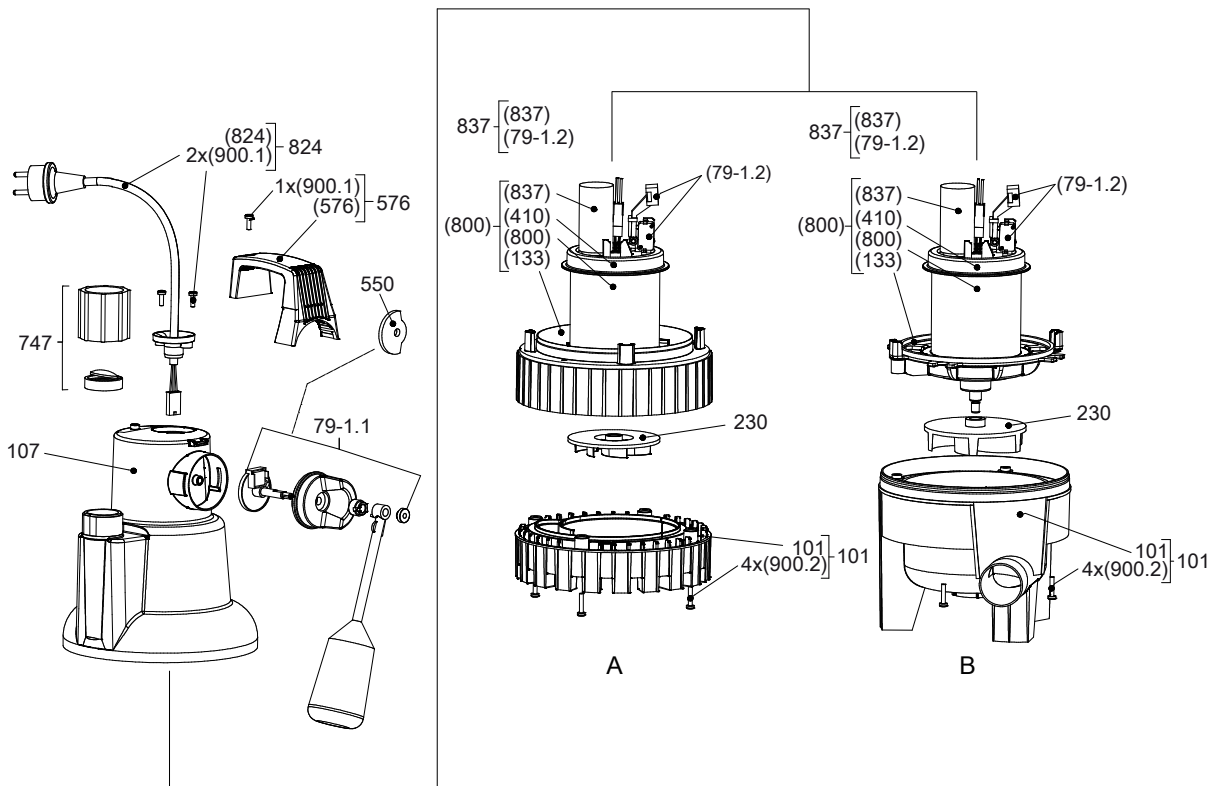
Explosionszeichnung A = DVV 3, B = DVV 4
